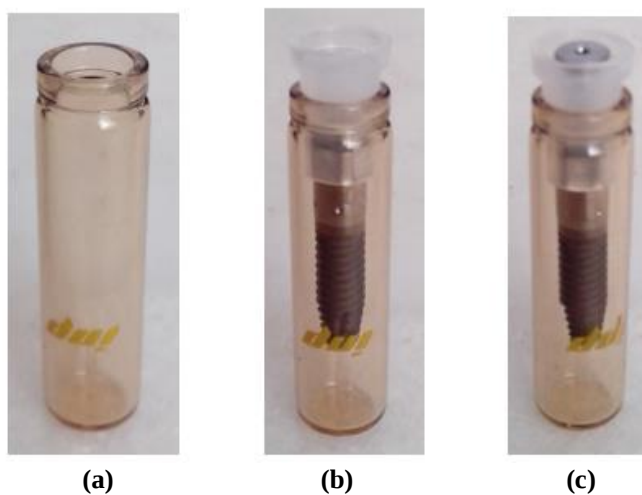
Montagem Frasco de Implante Dentário. (a) frasco interno; (b) frasco interno montado com o conjunto implante e tampa interna; (c) tapa implante colocado na tampa de frasco interno – Fonte: SISTEMA INP (dados internos).
